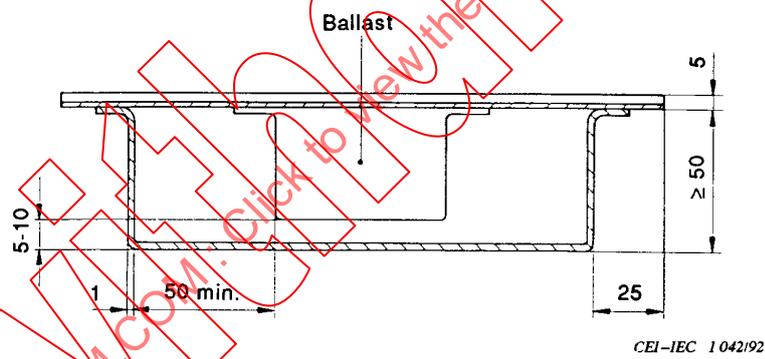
Boîtier d'essai pour l'essai d'échauffement du ballast
